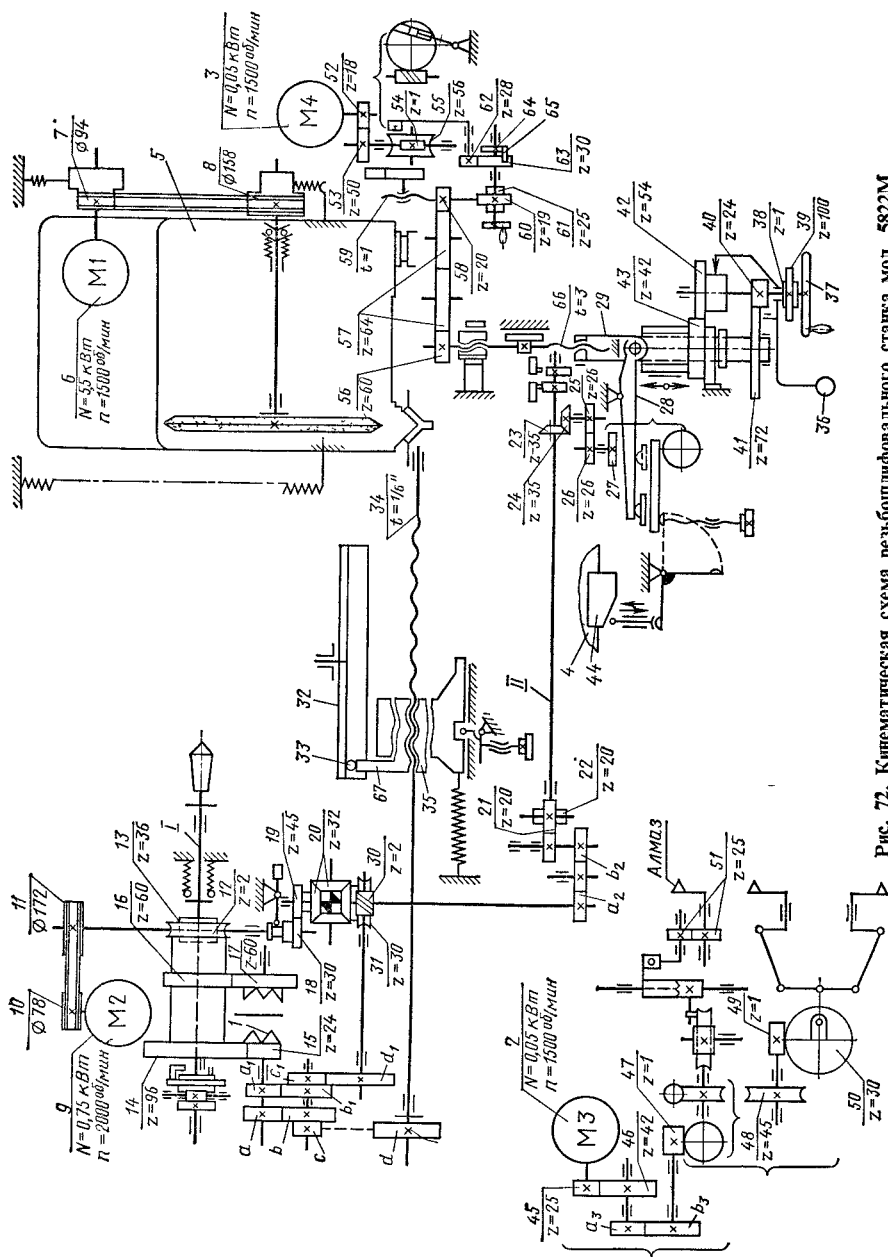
Кинематическая схема резьбошлифовального станка мод. 5822М
